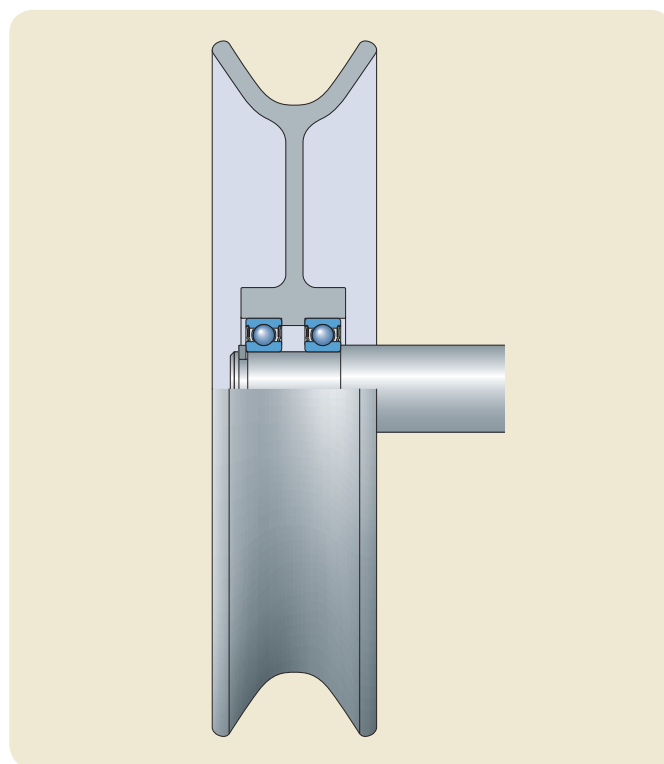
Disposición de rodamientos de la polea para cuerda.
